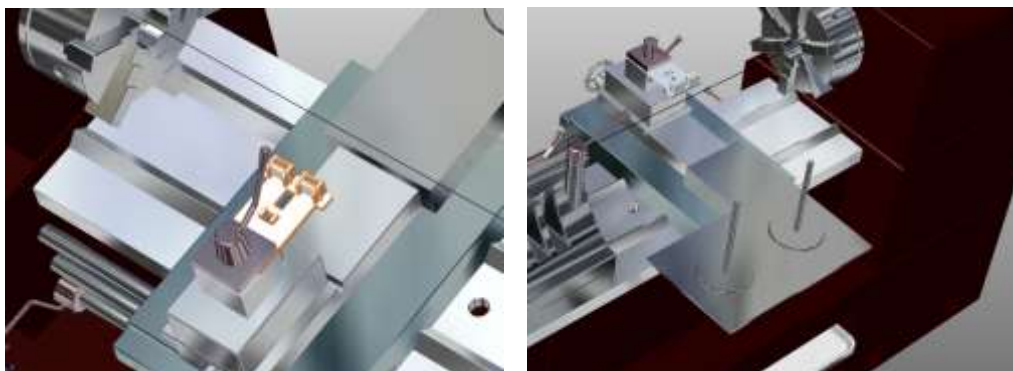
Приспособление для изготовления элементов каркаса установленный на станок
